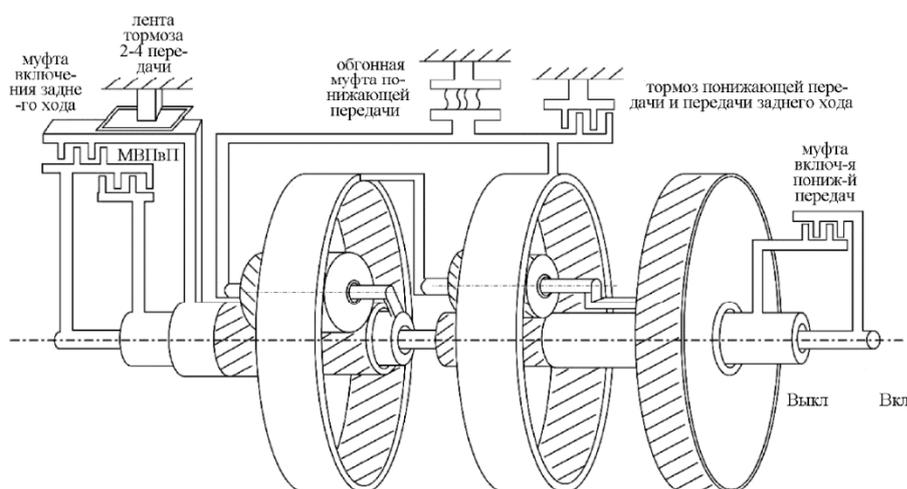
Кинематическая схема автоматической коробки передач LADA GRANTA
